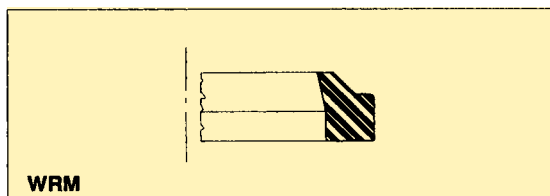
Raschiatore in gomma per montaggio in sede chiusa.
